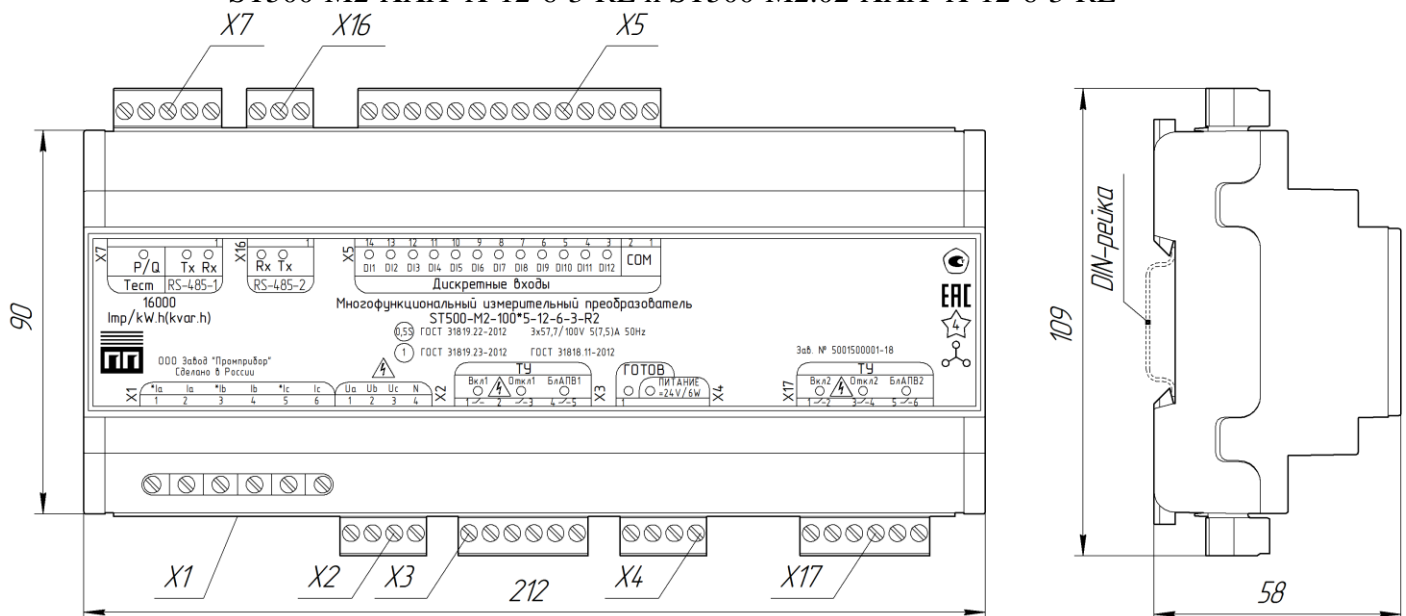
Внешний вид и габаритные размеры МИП ST500-M2-XXX*X-12-6-3-R2 и ST500-M2.02-XXX*X-12-6-3-R2
